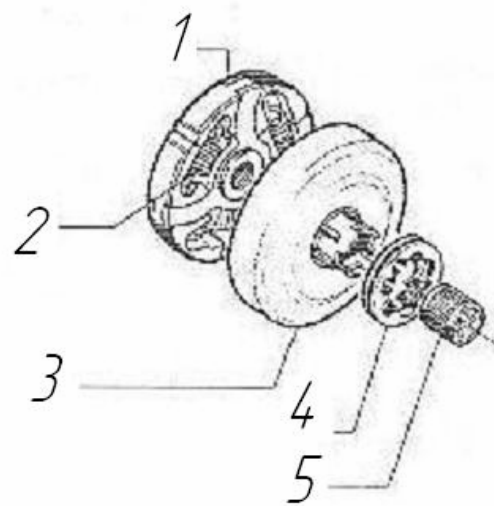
Муфта зчеплення: 1 – стискна пружина; 2, 3 – диски зчеплення; 4 – ведуча шестерня ланцюга; 5 – шліцева втулка
